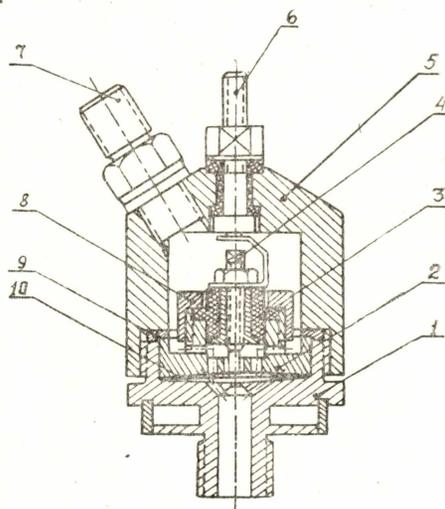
Одноконтактный датчик; 1 — корпус датчика; 2 — верхний ограничитель; 3 — изолятор; 4 — неподвижный контакт; 5 — крышка датчика; 6 — контакт; 7 — ниппель; 8 — гайка; 9 — прокладка; 10 — мембрана.
